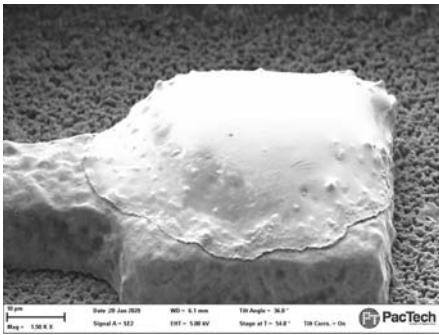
Restlotstruktur auf dem PCB Kontakt eines getrennten Chip on Board Assembly
